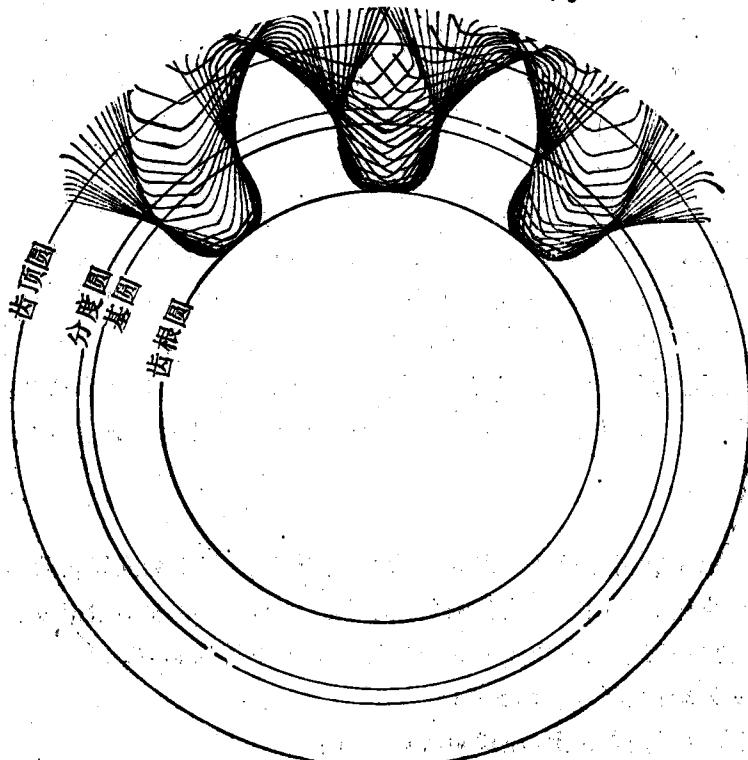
用直齿条刀具切制渐开线齿轮时,刀具齿廓的包络线即为标准渐开线齿轮的齿廓。
